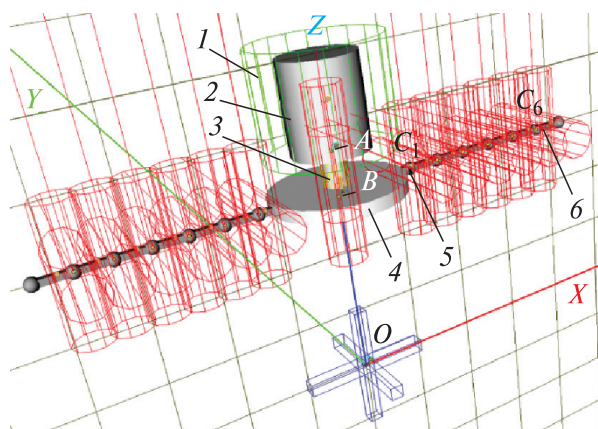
Компоночно-кинематическая схема ротора кустореза: 1 — корпус двигателя; 2 — ротор двигателя; 3 — фланец; 4 — ротор кустореза; 5 — проушины; 6 — лезвия
